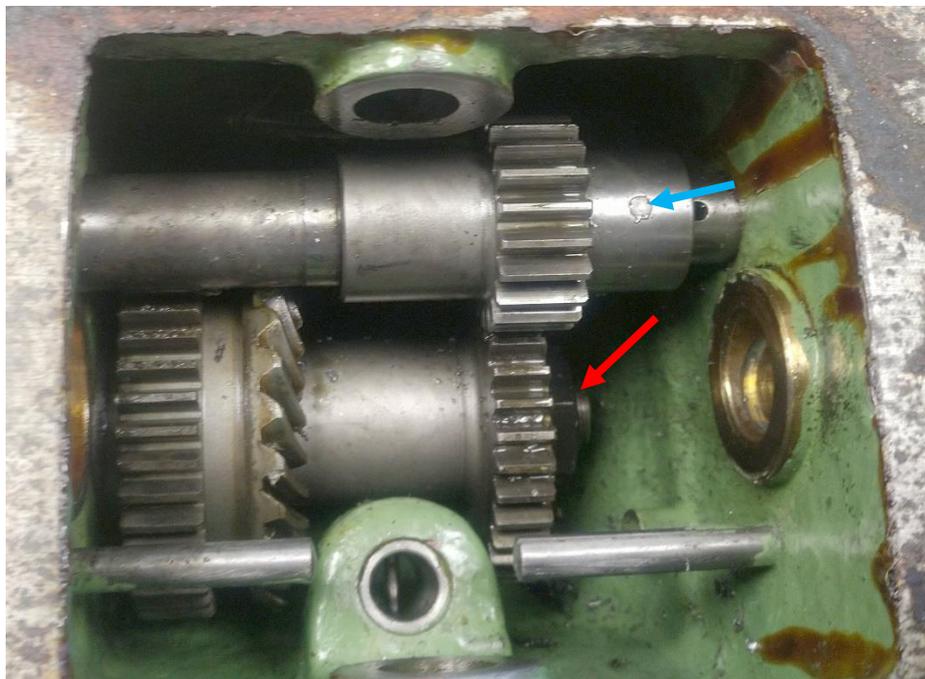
die Z-Spindel ist mit einer 22mm Sechskantschraube gesichert (roter Pfeil)
